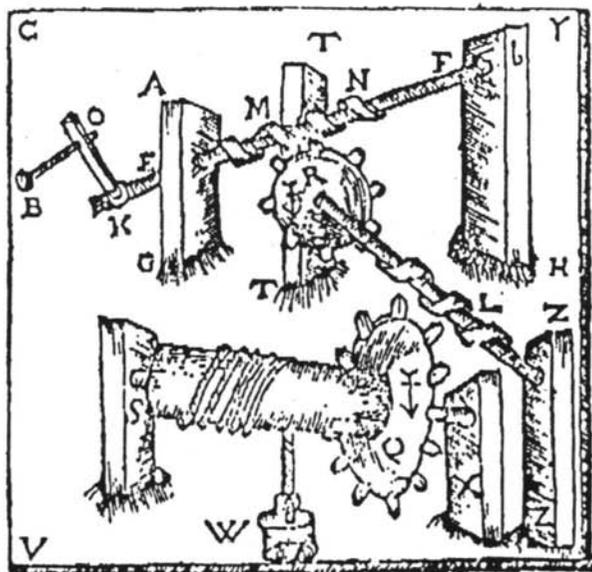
Elevadora manual con engranaje de tornillo sin fin
